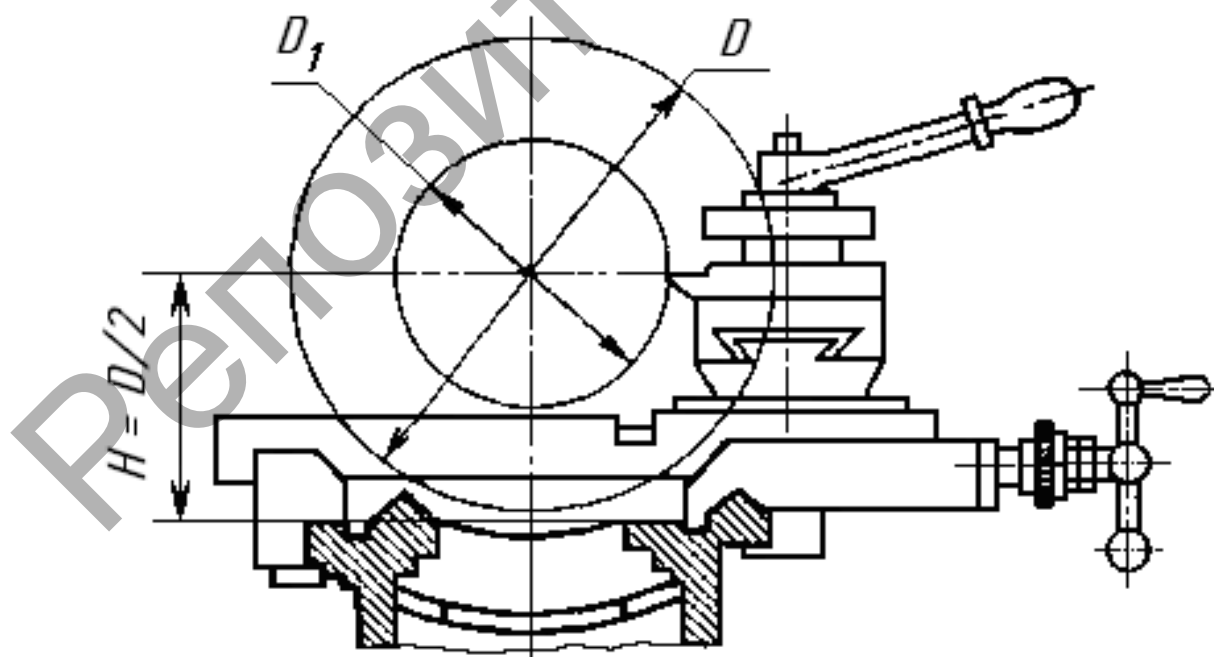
Габариты обрабатываемых на станке заготовок
